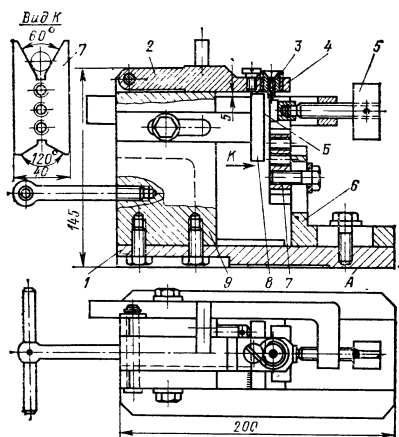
Переналаживаемый кондуктор для сверления радиально расположенных отверстий во втулках и гайках
